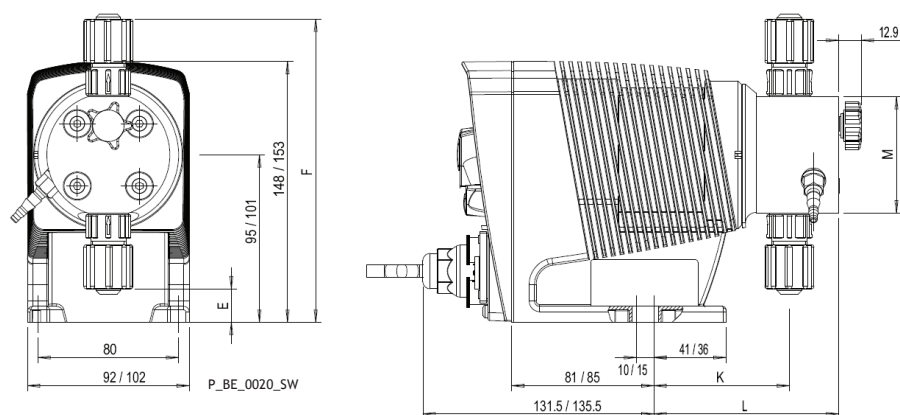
Размерный чертеж Beta® BT4b/BT5b, Материал конструкции NV
